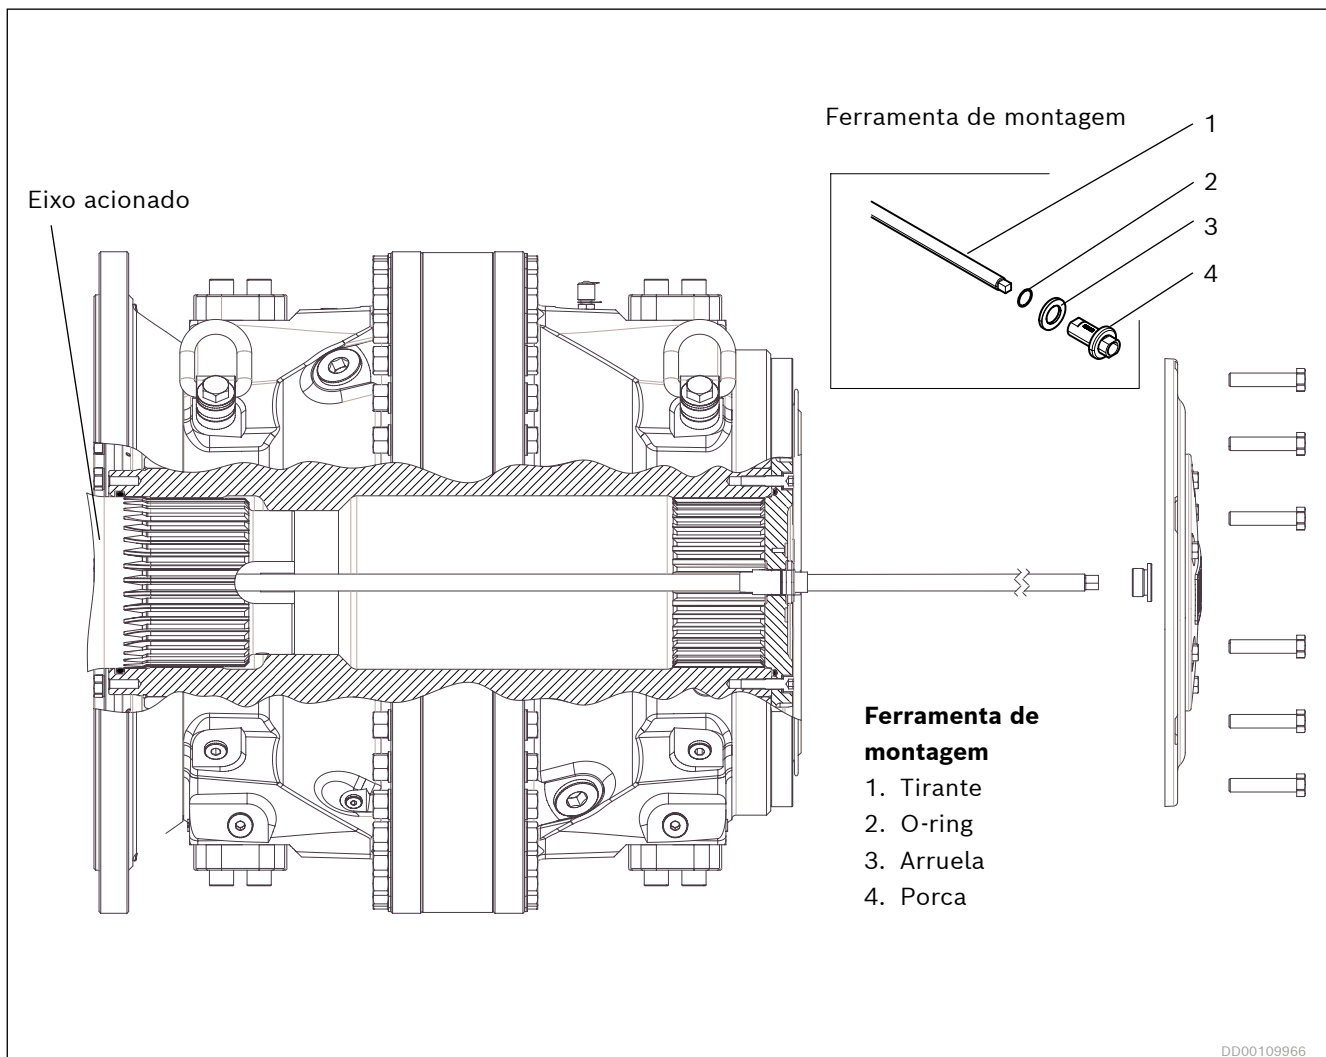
Montagem do motor CBp com a ferramenta de montagem
